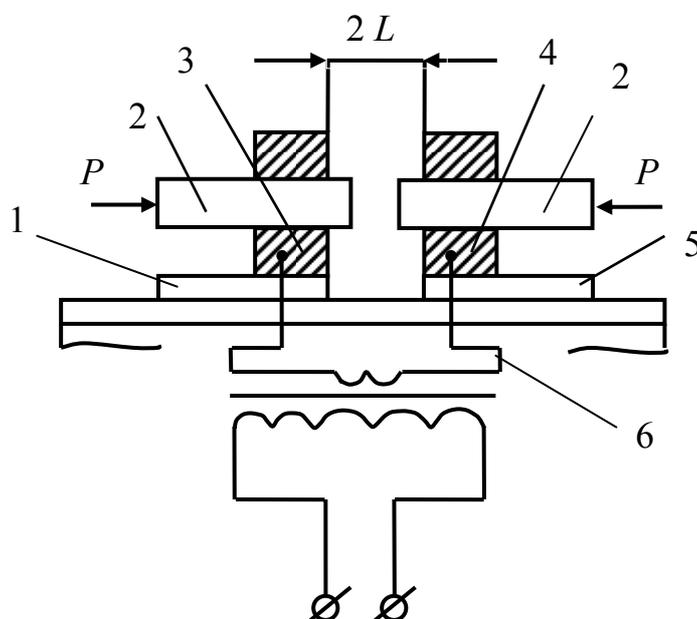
Схема стыковой сварки: 1 – неподвижная плита; 2 – свариваемые детали; 3 – зажим на неподвижной плите; 4 – зажим на подвижной плите; 5 – подвижная плита
